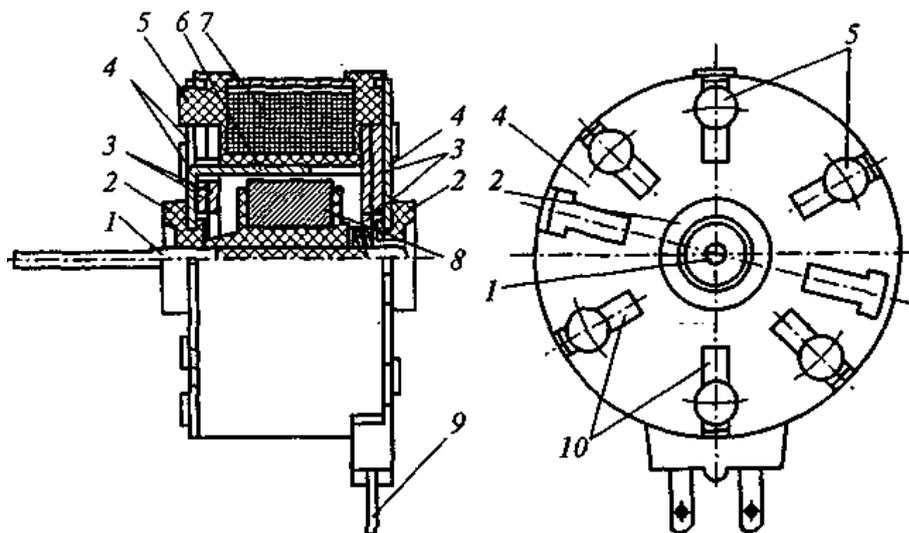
Однофазный многополюсный двигатель типа ДСО-32 с экранированными полюсами: 1 – вал; 2 - подшипники скольжения; 3 – медная пластина; 4 – магнитопроводы; 5 – шпильки; 6 – полюс; 7 – катушка; 8 – постоянный магнит; 9 – зажимы; 10 – пластины
